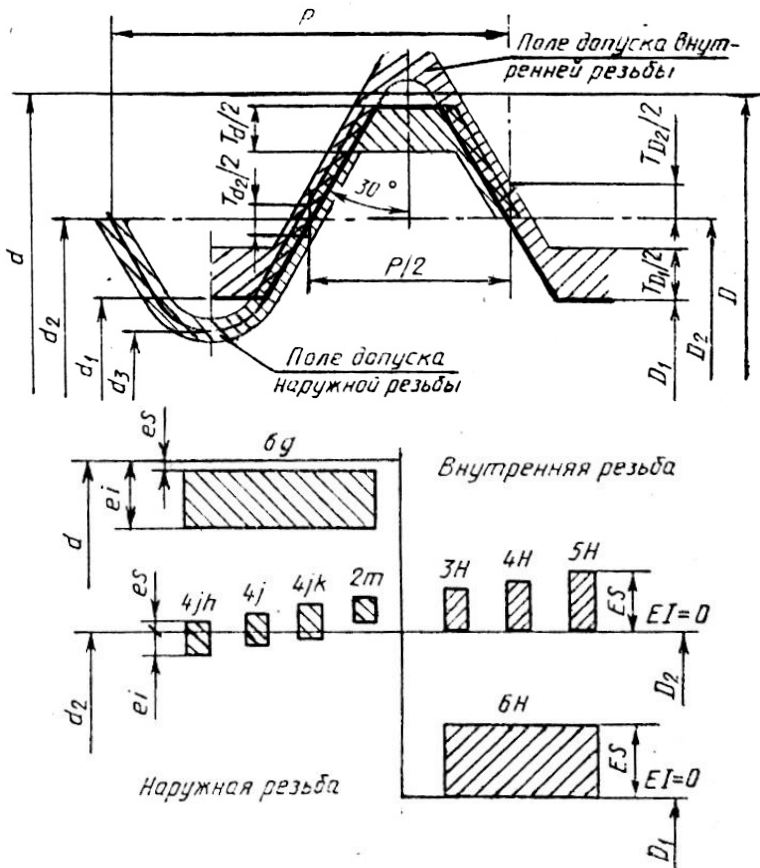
Расположение полей допусков наружной и внутренней резьбы:
